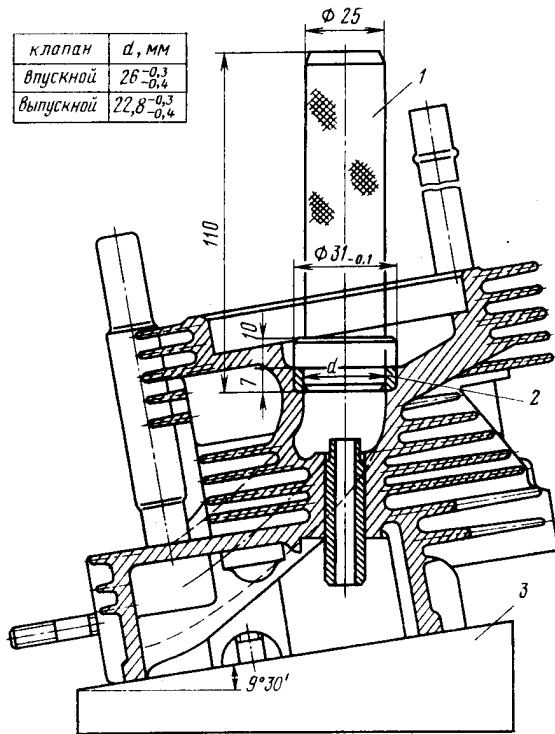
Оправка для запрессовки седла клапана: 1 — оправка; 2 — седло клапана; 3 — подставка
